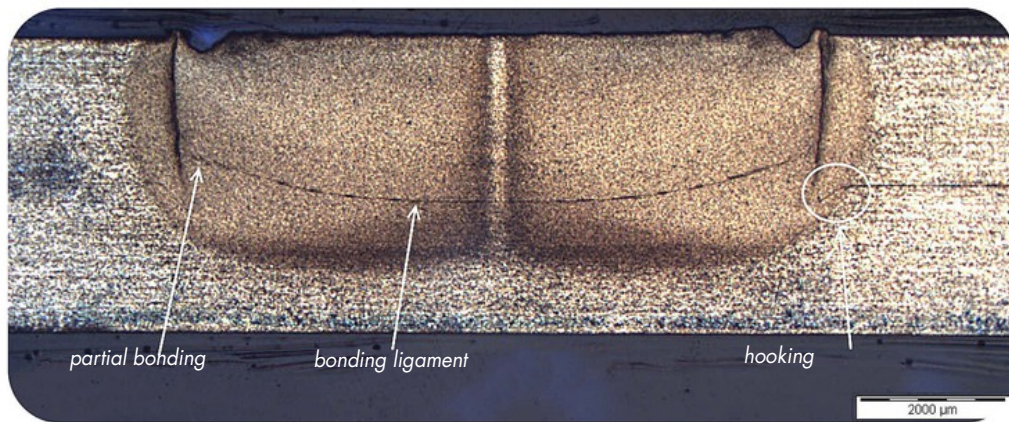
coupe de soudage typique dans l'aluminium EN AW-6082-T6 (épaisseur de tôle: 2 mm)
